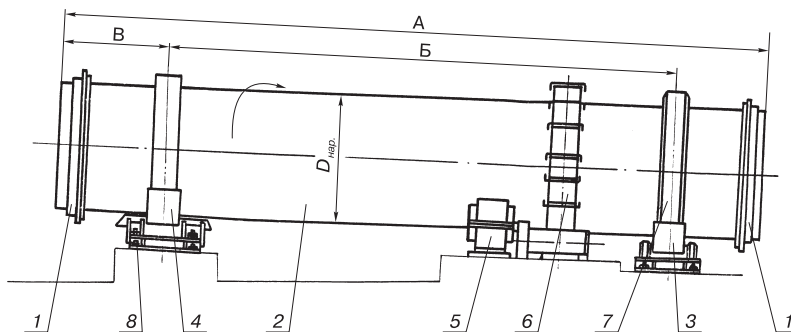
Сушильный барабан: 1 – уплотнение; 2 – корпус; 3 – станция опорная; 4 – станция опорно-упорная; 5 – привод; 6 – шестерня венцовая; 7 – бандаж; 8 – ролик упорный
